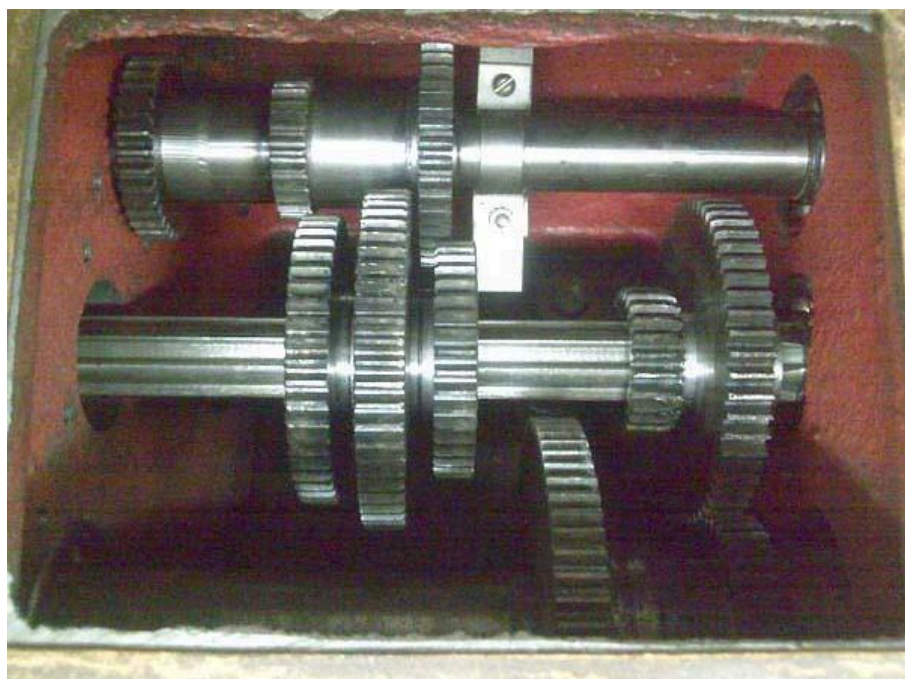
Коробка швидкостей верстата НГФ-110шЗ
